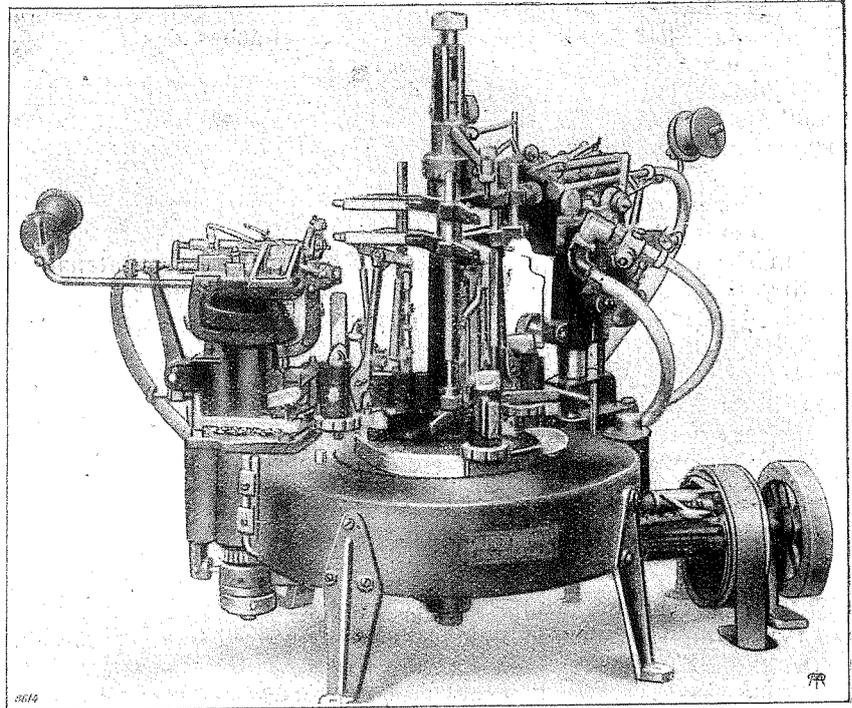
Vue d'une machine automatique à étoiler et perler.
